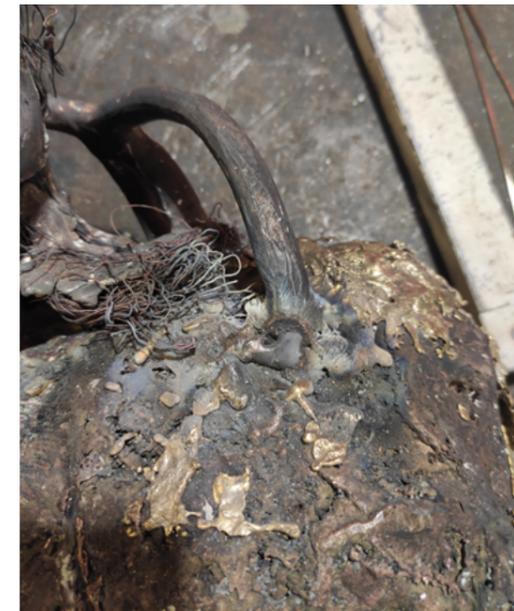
Diego Vidal. Soldando la cabeza al torso.
